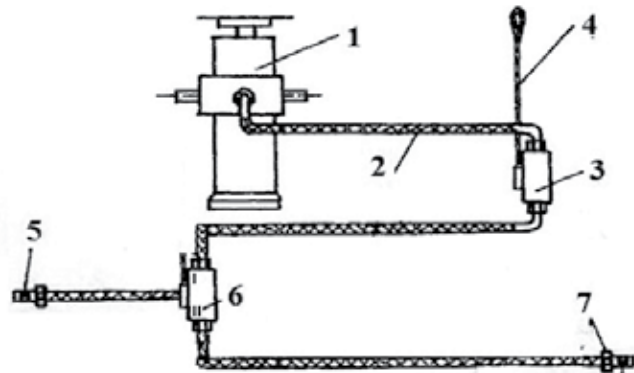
Schema der hydraulischen Ladekasten-Kippvorrichtung
